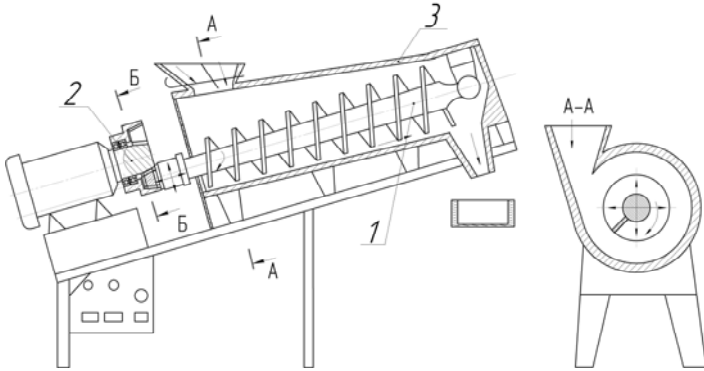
Конструкція гвинтового конічного змішувача: 1 – ГРО; 2 – планетарна передача; 3 – кожух
